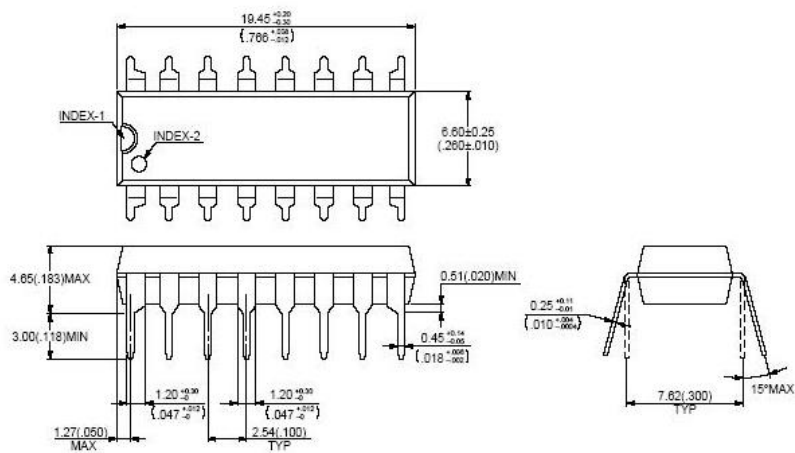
Габаритні розміри мікросхеми MM5368
